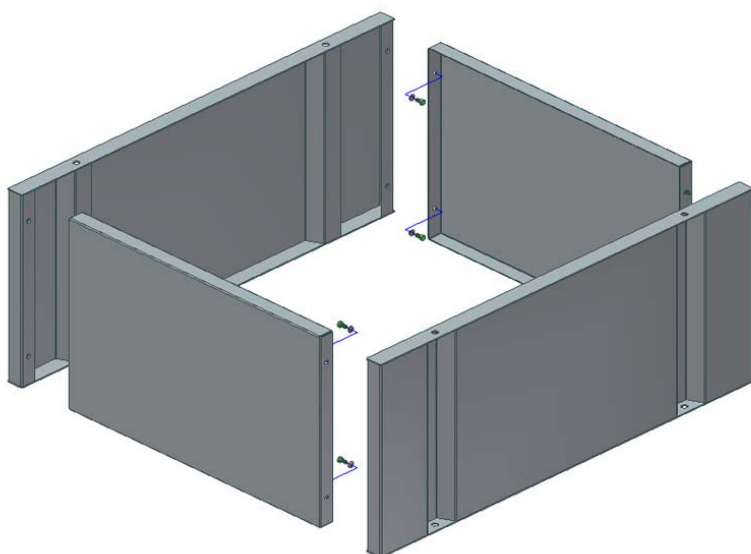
Mesa de máquinas herramienta de borrador de montaje
